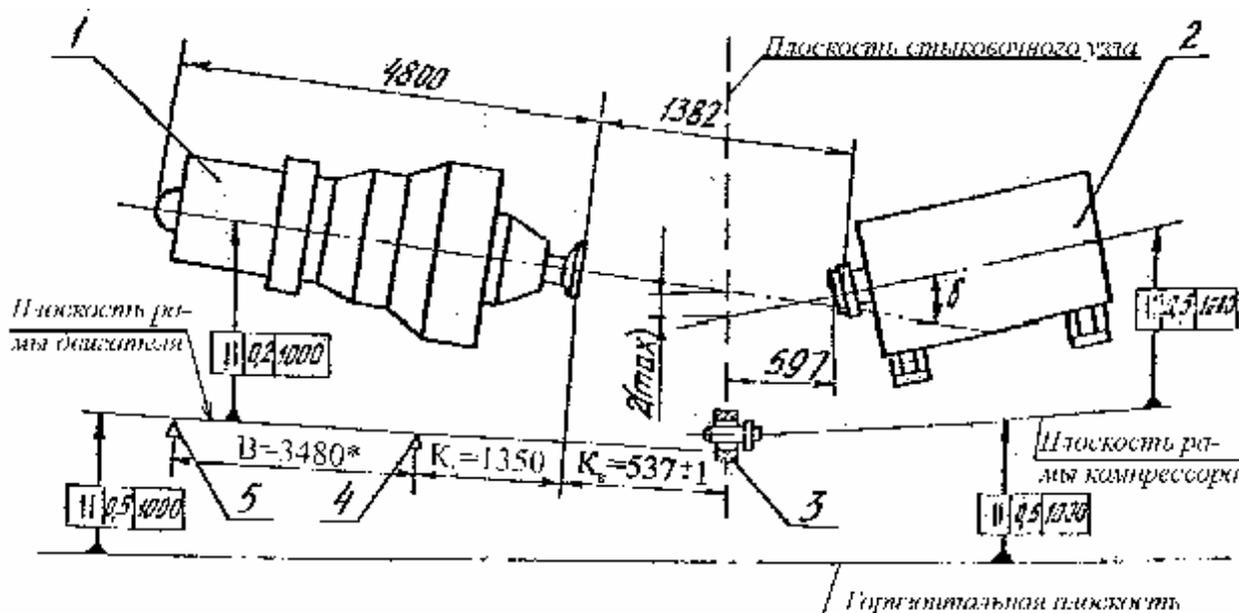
Схема расположения двигателя и компрессора после монтажа
